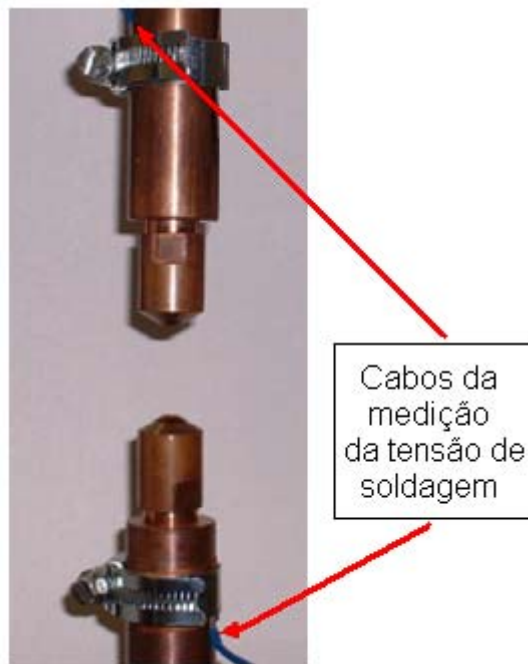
Fixação dos cabos para medição da tensão de soldagem
